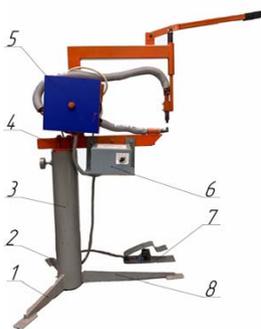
Лабораторная стойка для контактной сварки:
